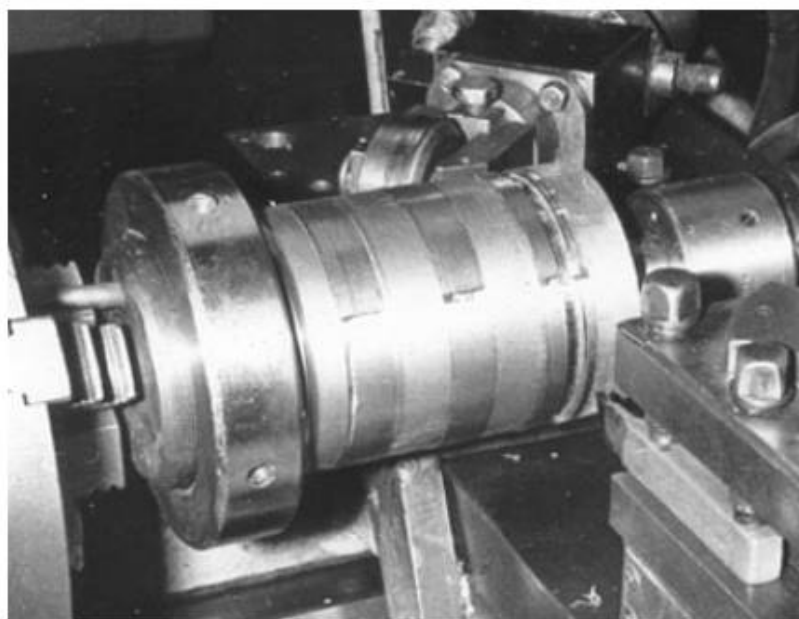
Общий вид оправки для разрезания цилиндрического изделия, установленной на токарном станке
